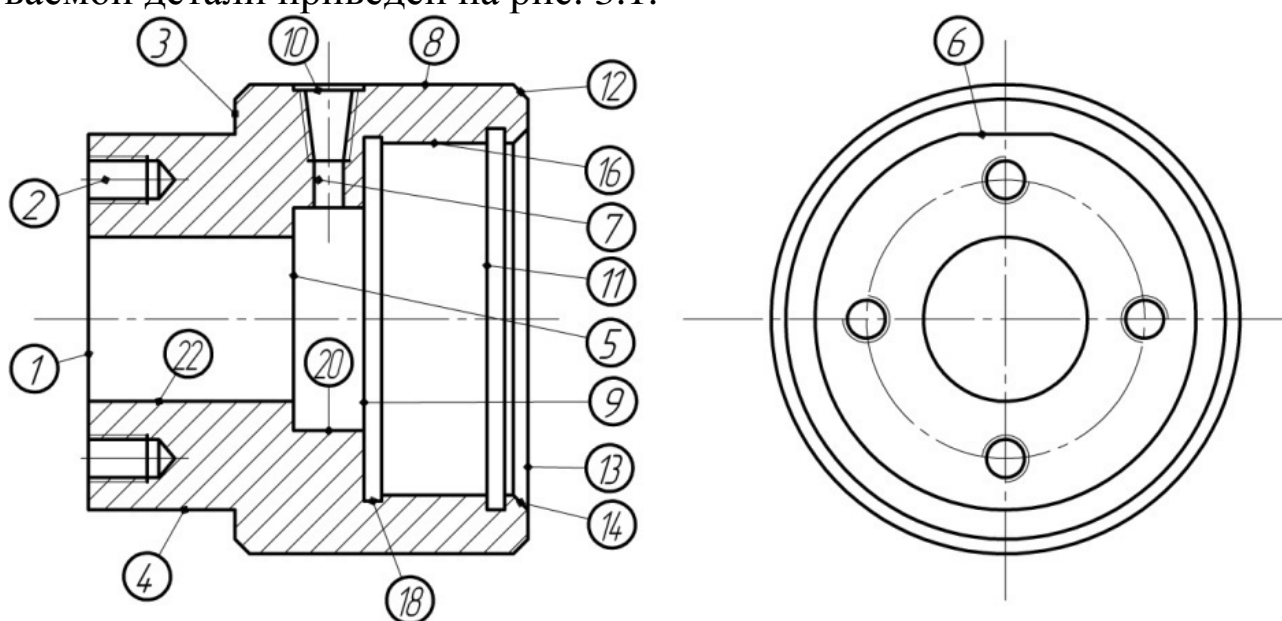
Нумерация обрабатываемых поверхностей детали
